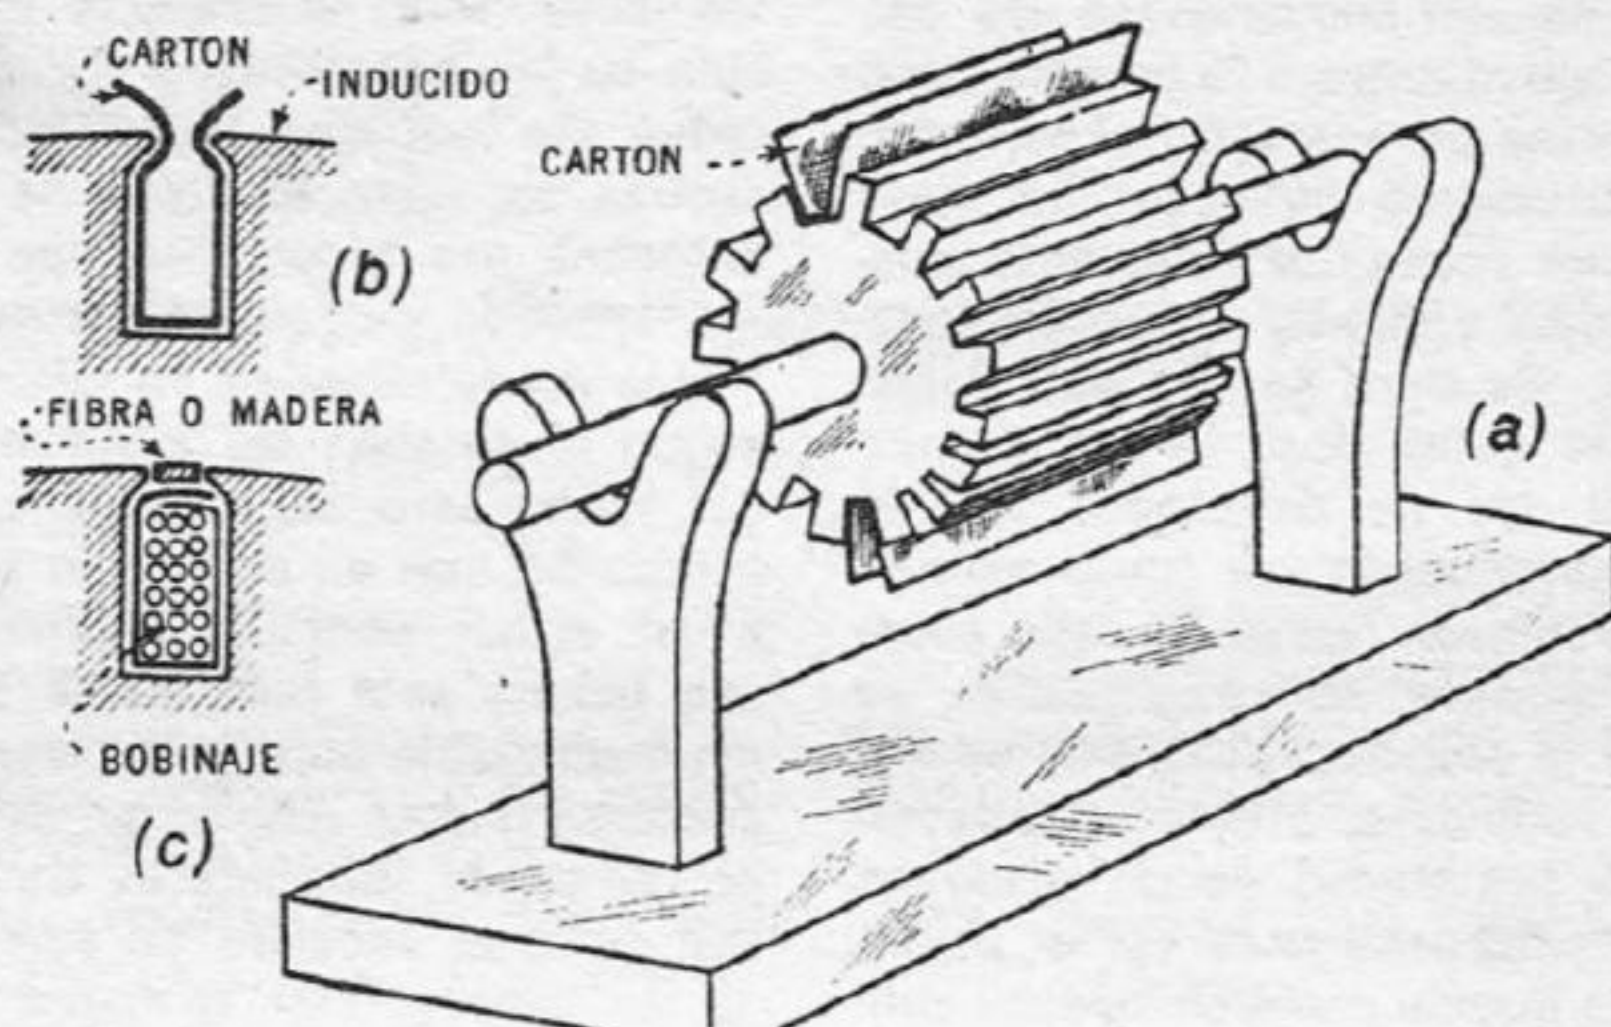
Aspecto del caballete que se emplea para hacer el devanado de los bobinajes.
